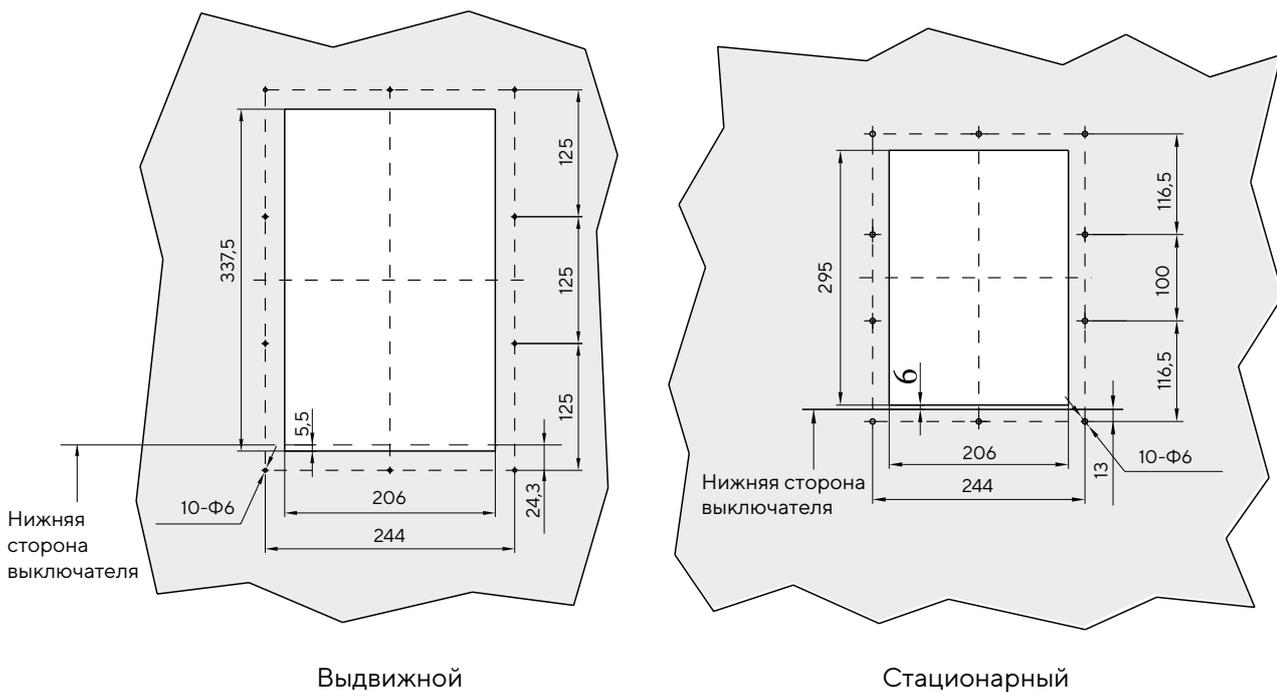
Габаритные размеры рамки обрамления выреза в двери для выключателей типоразмера S
